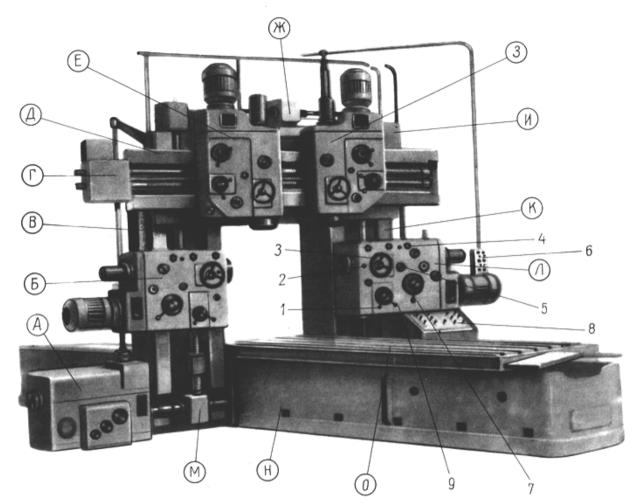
Общий вид продольно-фрезерного станка модели 6652
